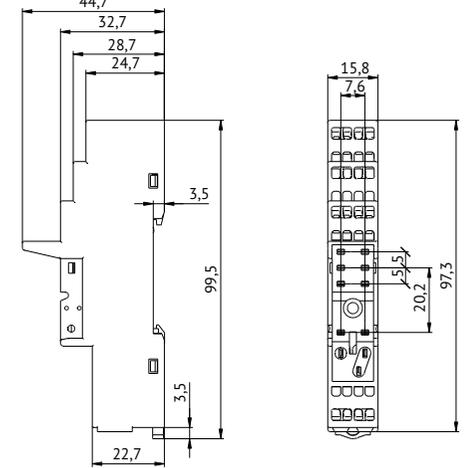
Габаритные, установочные и присоединительные размеры розетки OptiRel G RR95-52
